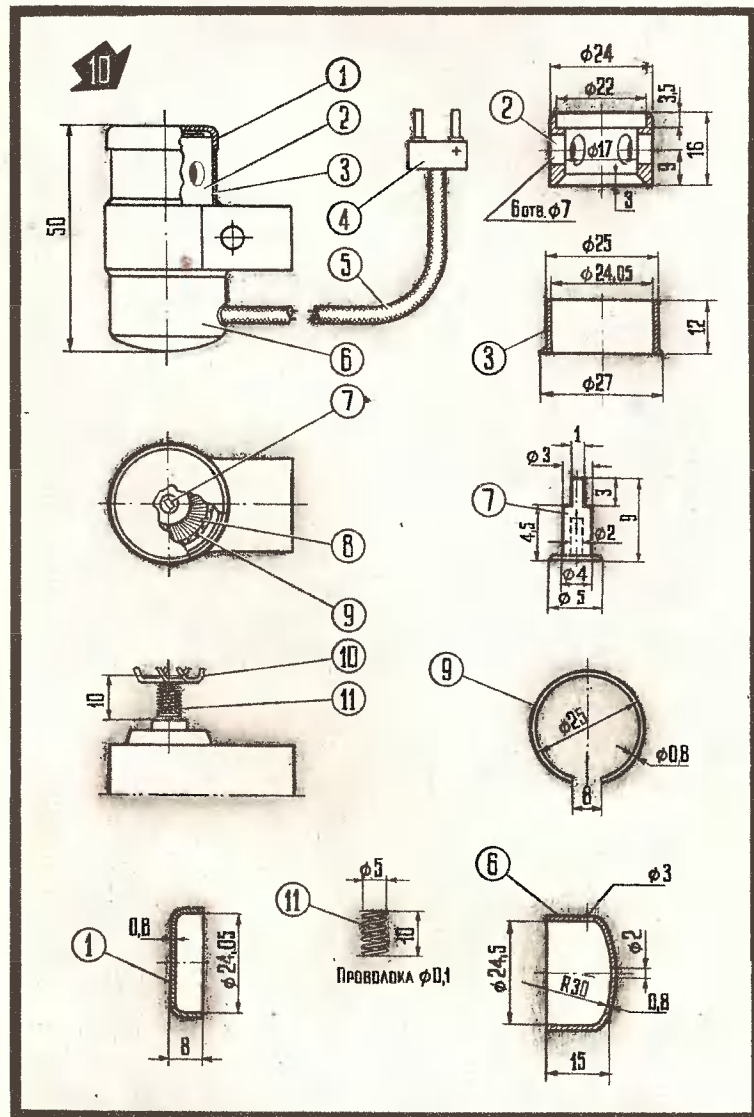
Бритва в сборе и ее детали: 1 — крышка; 2 — опорное кольцо из органического стекла, которое приклеивается к корпусу двигателя клеем БФ-2; 3 — защитное дюралюминиевое кольцо, надеваемое на опорное кольцо (скользящая посадка); 4 — вилка; 5 — провод; 6 — крышка двигателя; 7 — наконечник оси двигателя (приклеивается к оси клеем БФ-2); 8 — неподвижный нож (направляющая бритвы типа «Харьков»); 9 — опорное кольцо неподвижного ножа; 10 — подвижный (вращающийся) нож; 11 — поджимная пружина.
